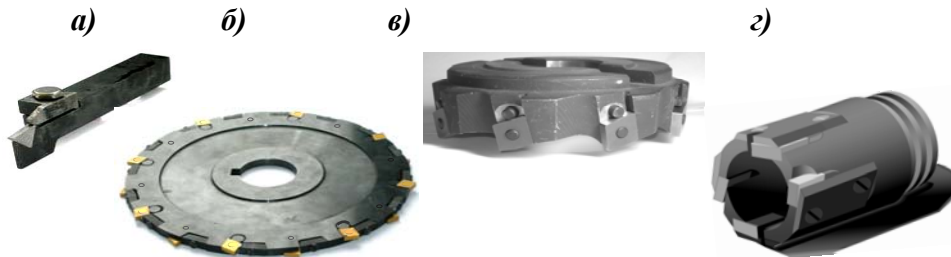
Виготовлені та випробувані нові види різальних інструментів з боковою установкою і кріпленням БНП: а) відрізнi різці, б) дискові і відрізнi фрези, в) торцеві фрези, г) головки кільцевих свердел для глибокого свердління
